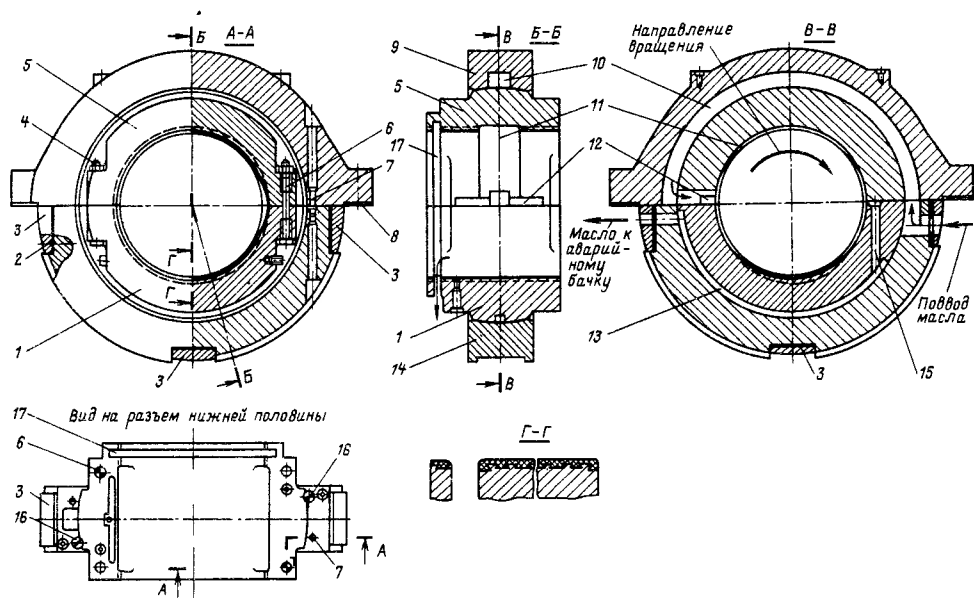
Опорный подшипник с самоустанавливающимся вкладышем конструкции ХТЗ:
